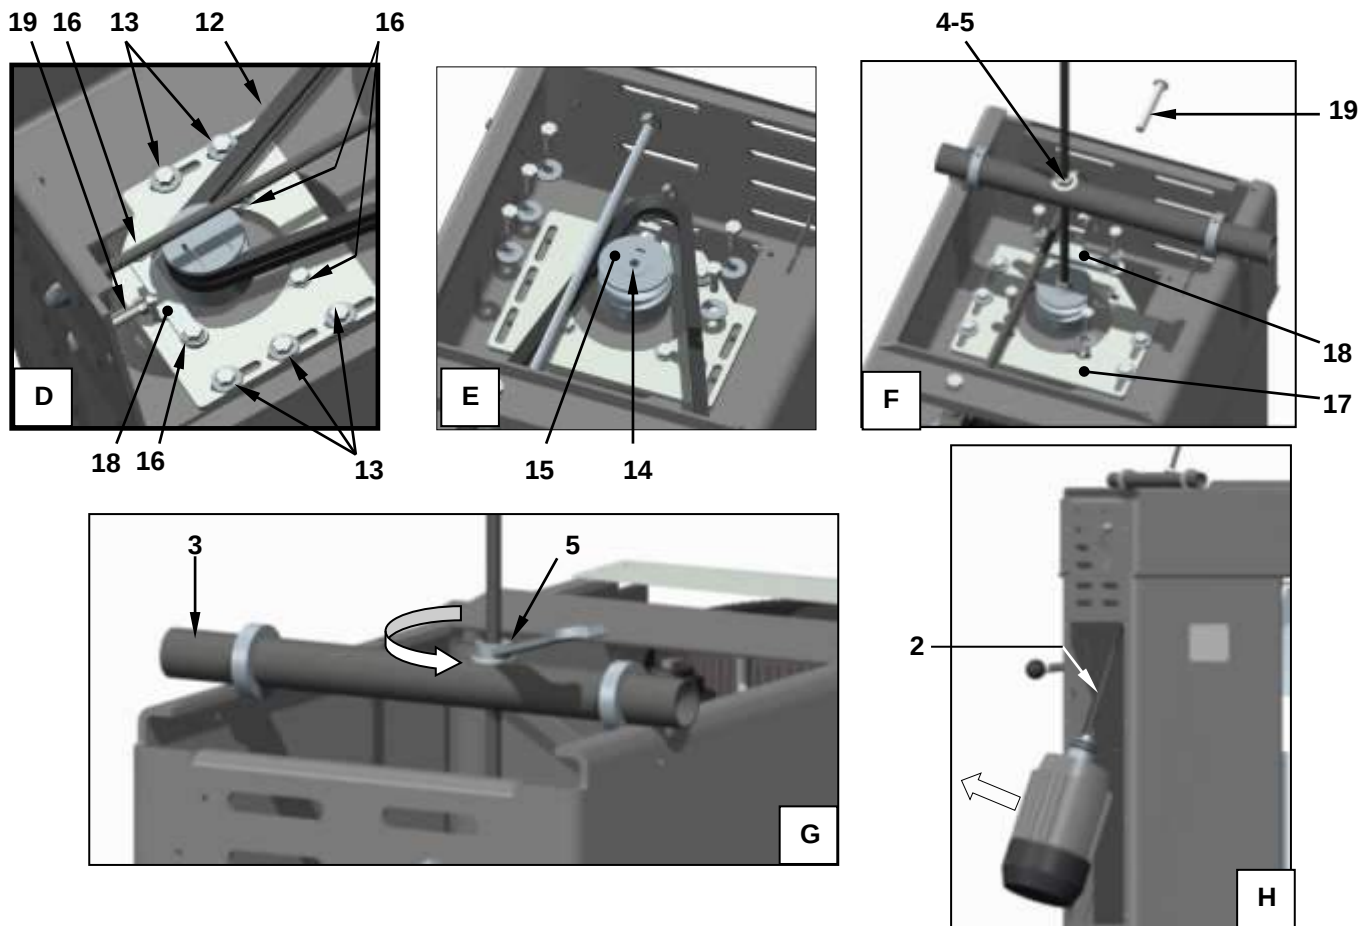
Demontage/Montage des Werkzeug-Motors (PL30 - PL40 - PL60)
